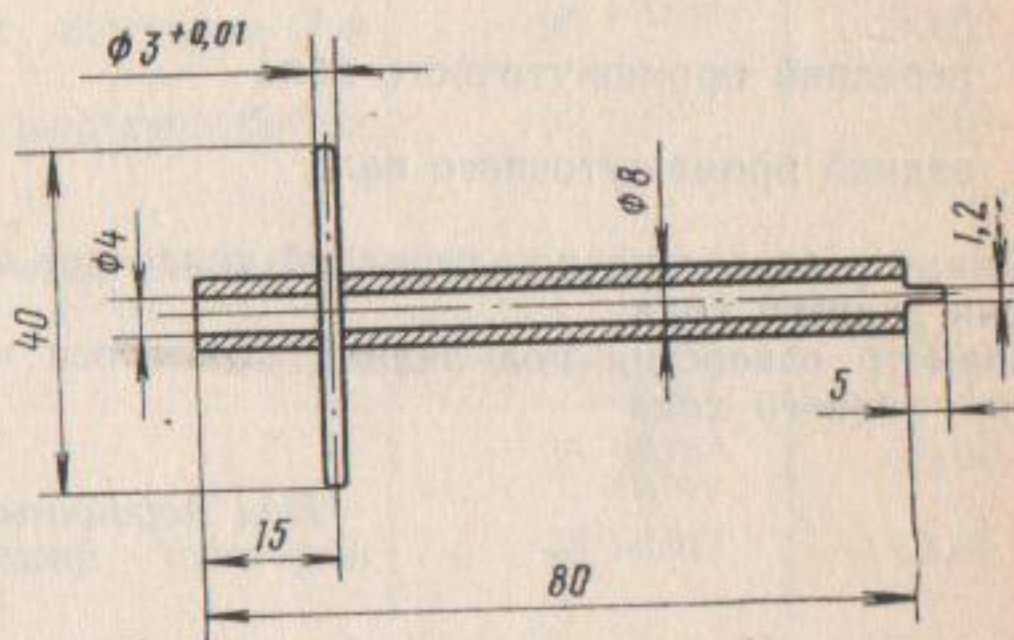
Ключ для разборки корпуса блока электропневматических клапанов
